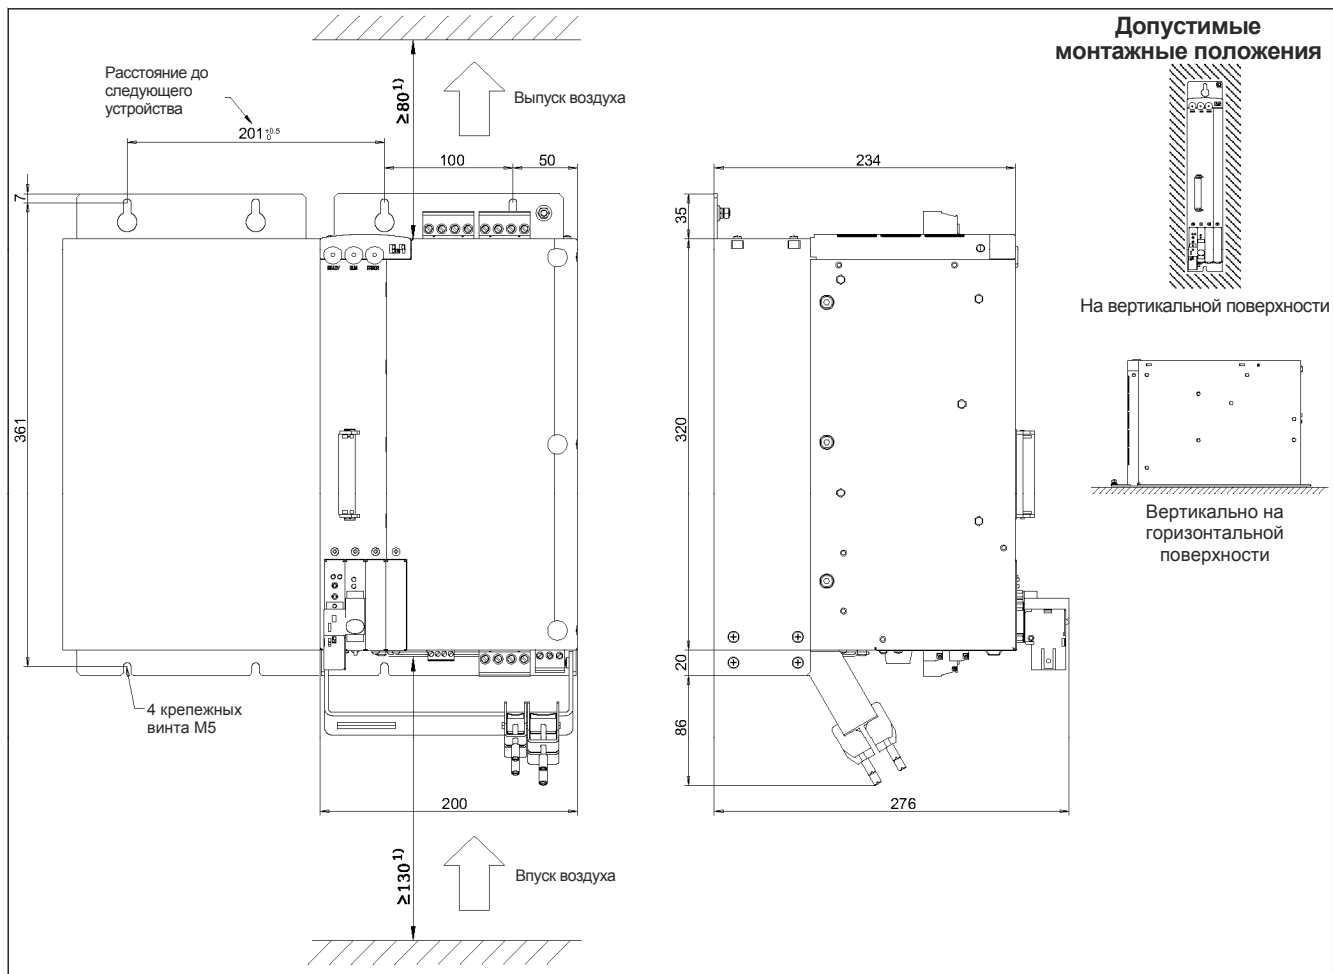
АСОPOS 1180, 1320 – Габаритный чертеж и монтажные размеры
